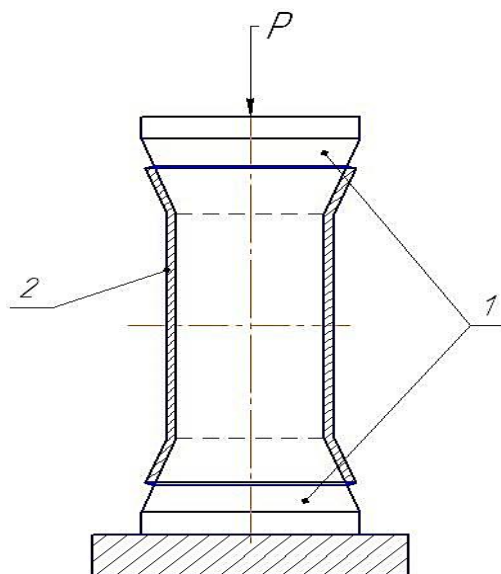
Раздача (осадка) цилиндрической заготовки:
